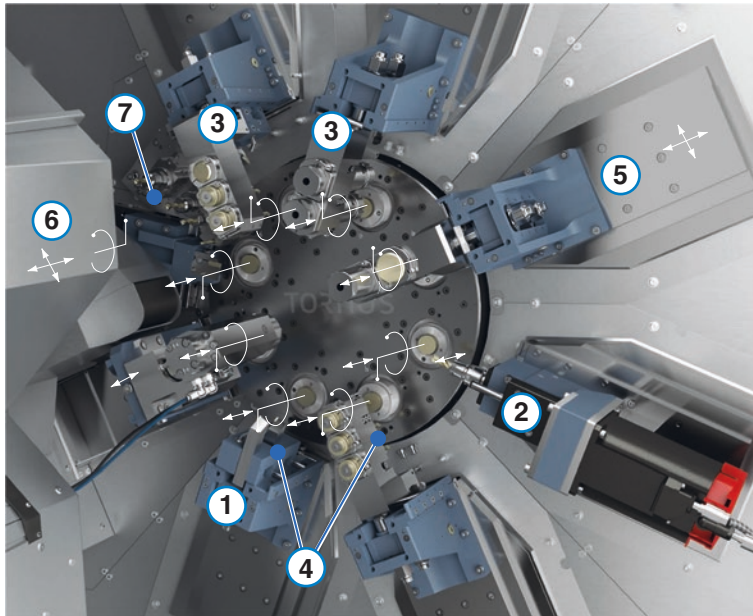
Arbeitsraum der Multi-Swiss 8x26 mit aufgebauten Werkzeugträgern. [Bildquelle: Torn17]
